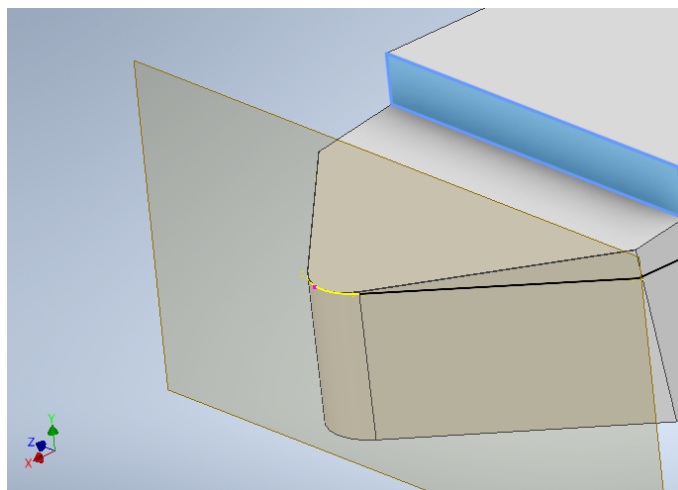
Criação do primeiro Plano Auxiliar3, ou Plano de Trabalho
